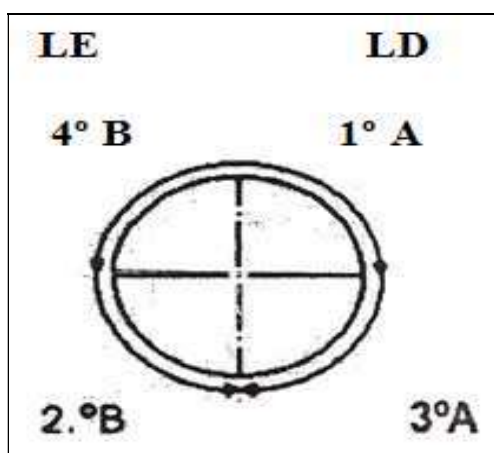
Sequência de soldagem (dois soldadores)
